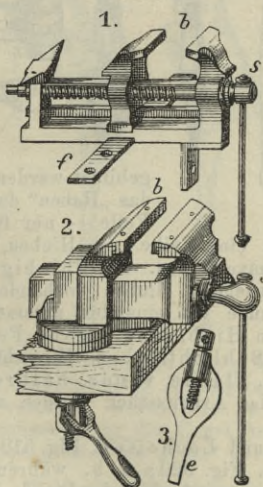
1. Schmiedeiserner Parallel-Schraubstock. — 2. Gusseiserner Parallel-Schraubstock zum Drehen. — 3. Dreherherz.
